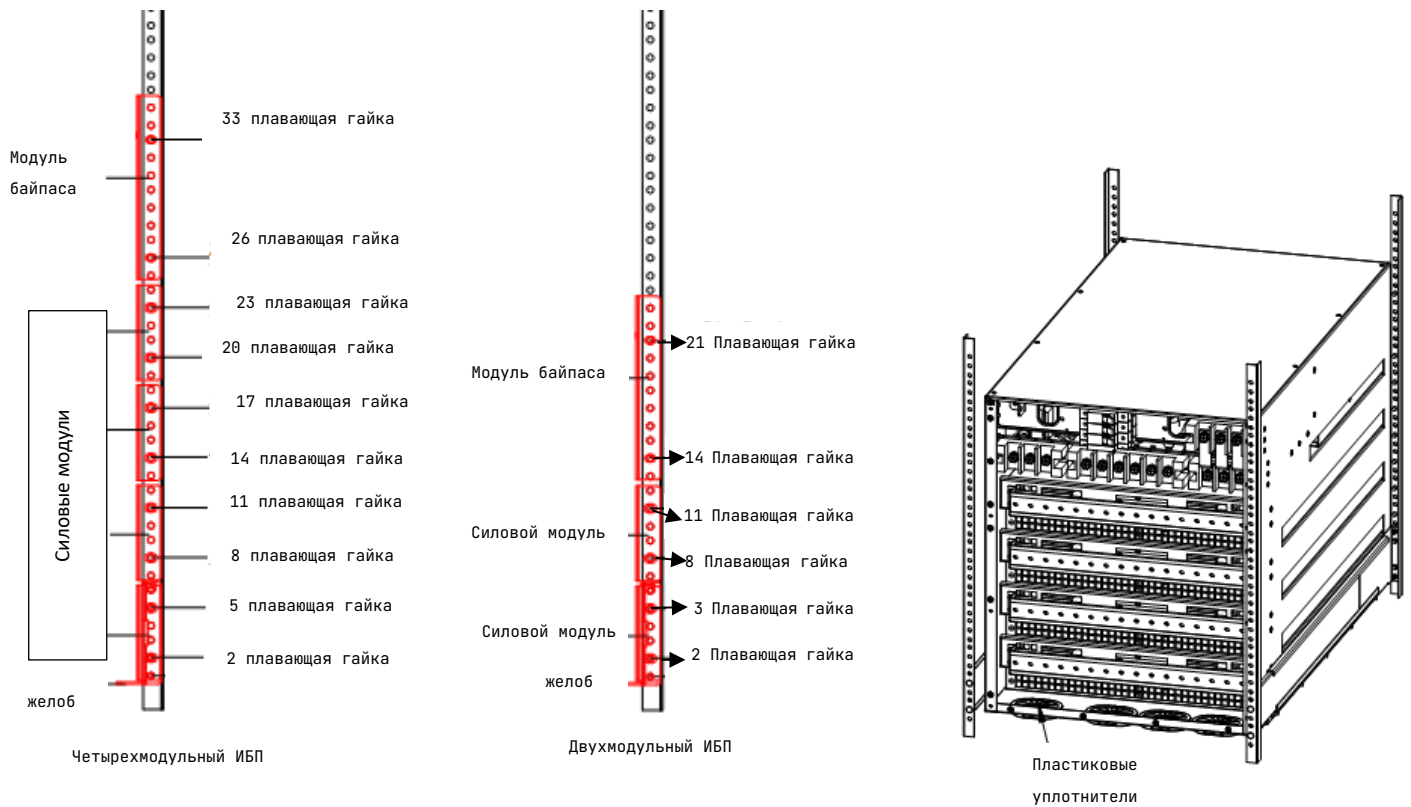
Установка в шкаф. Нумерация плавающих гаек
